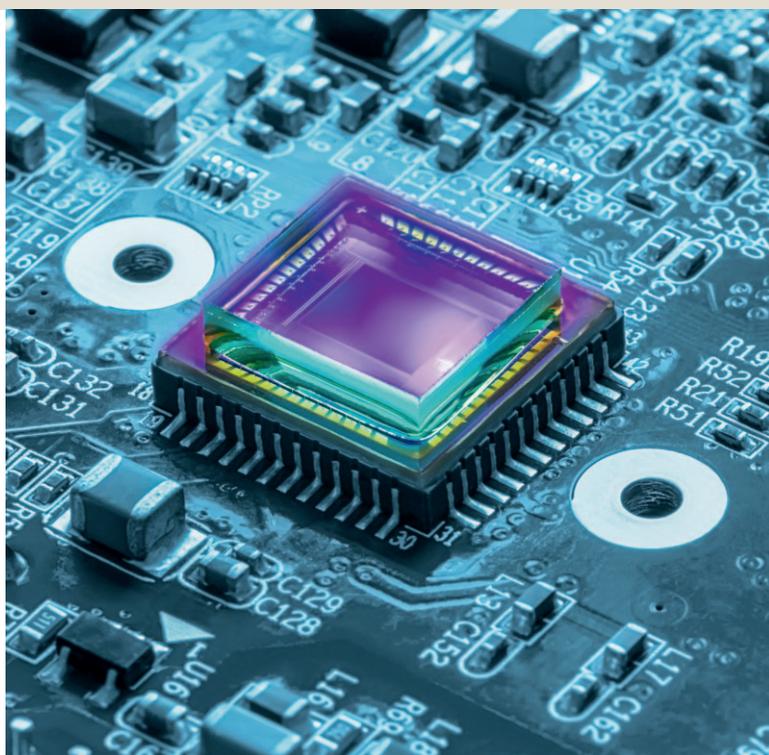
Laser-Glasschweißen kommt häufig im Bereich der Mikroelektronik zum Einsatz
